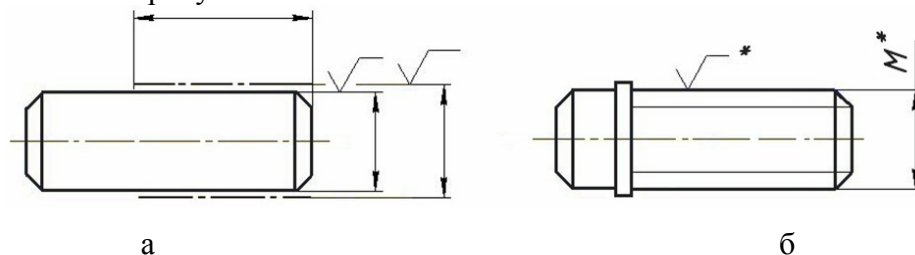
Обозначение шероховатости поверхности с покрытием
